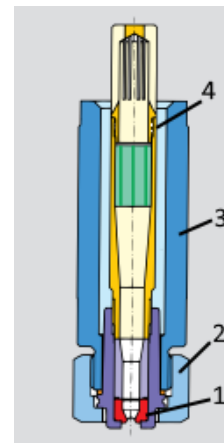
Форсунка фірми Lechler SCALEMASTER: 1 – форсунка; 2 – накидна гайка; 3 – ніпель; 4 – напрямний пристрій для потоку води на вході
